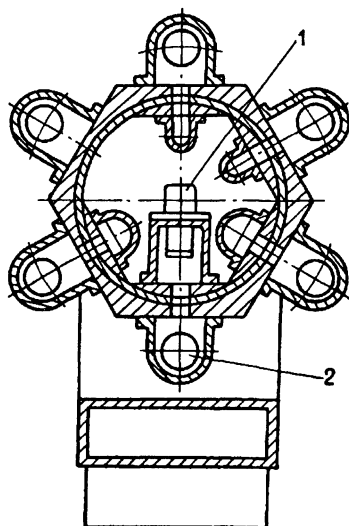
Установка УЛ112 (вид сбоку) для ЭЛС изделий массового производства
